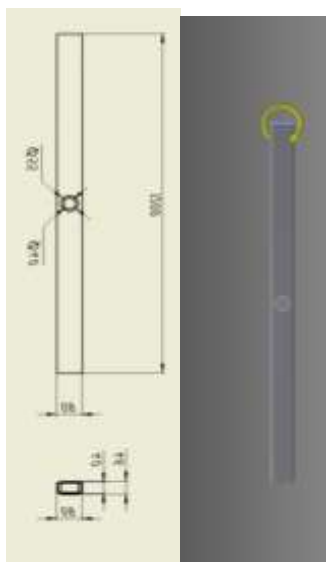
Номера профилей сечений Рис. 5 чертеж и 3D-модель схемы МКЭ
